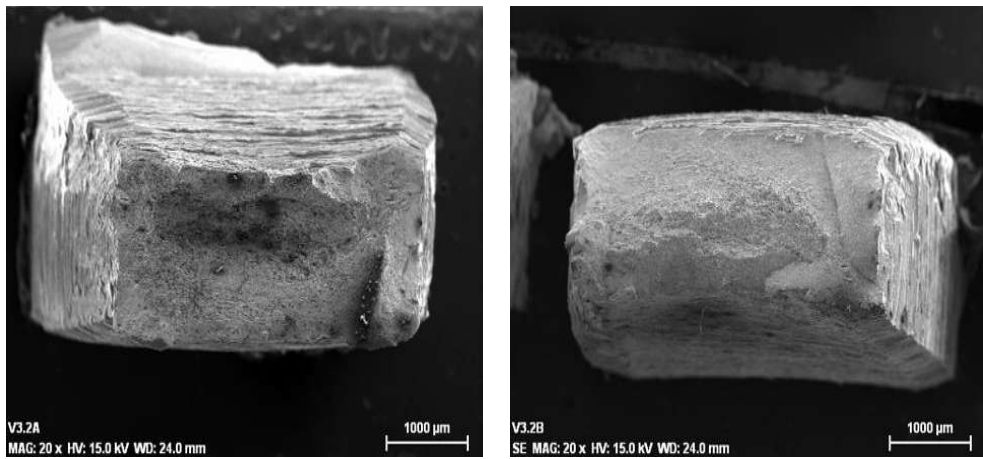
Fractografía de la unión a 75°, probeta 2.
